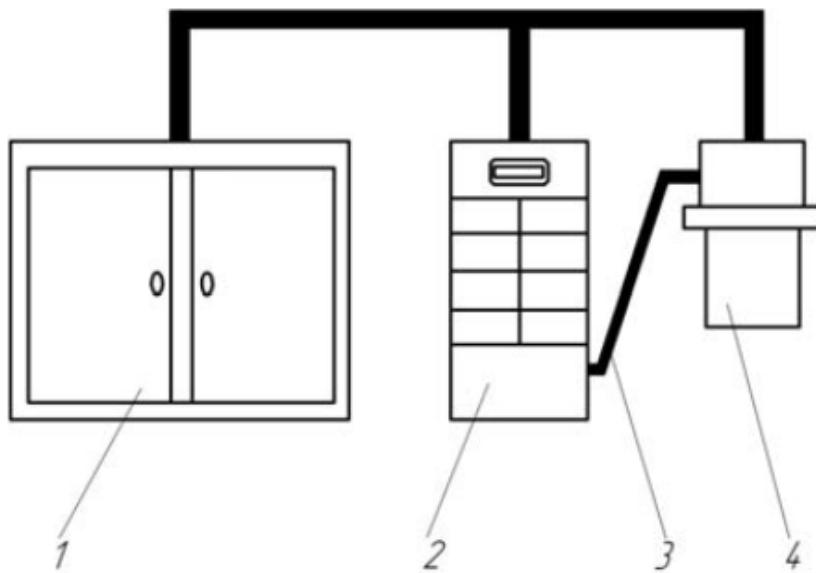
Состав энергоблока ЭЛУ для сварки
